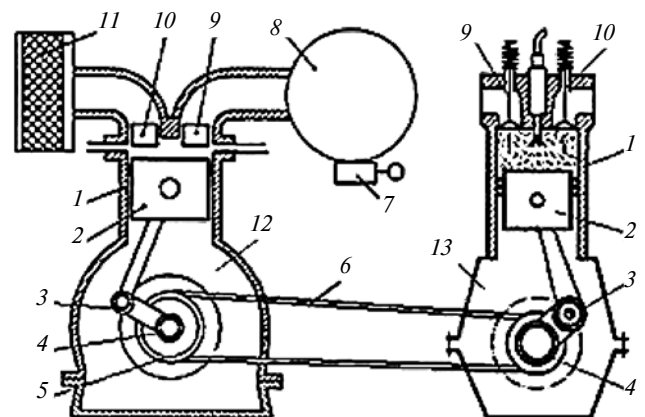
Мобильный агрегат для получения сжатого воздуха:
